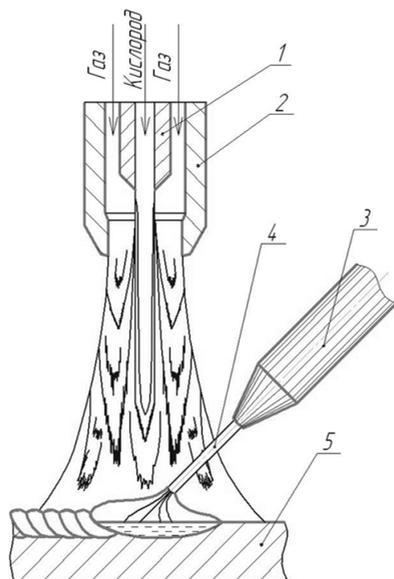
Схема сварки с газопламенной защитой:
